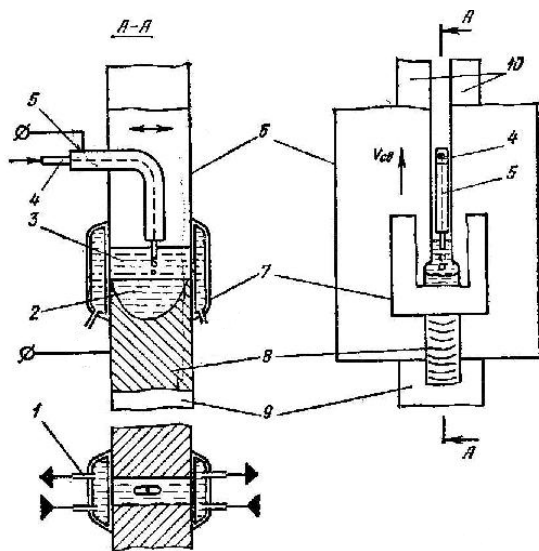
Схема электрошлаковой сварки: 1 – трубы ползуна, 2 – сварочная ванна расплавленного металла, 3 – шлаковая ванна, 4 – сварочная проволока, 5 – мундштук, 6 – основной металл заготовок, 7 – ползуны (формирующие устройства), 8 – затвердевший сварной шов, 9 – вводная планка, 10 – выходная планка
